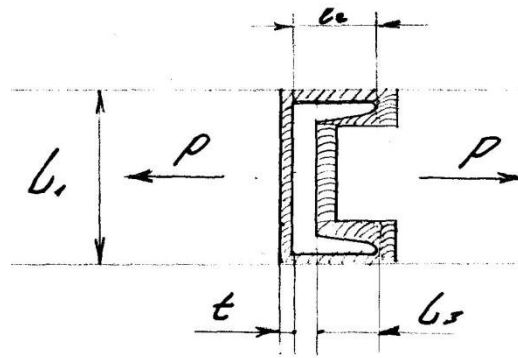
Розрахункова схема зварювального кріплення кронштейна до рами (вид загальний)
